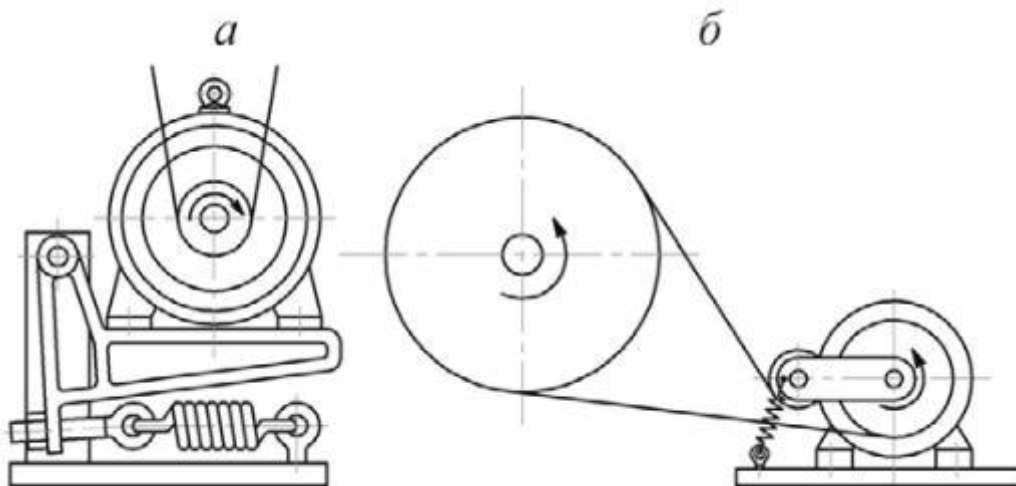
Способы автоматического натяжения ремня с использованием массы качающегося двигателя и пружины
